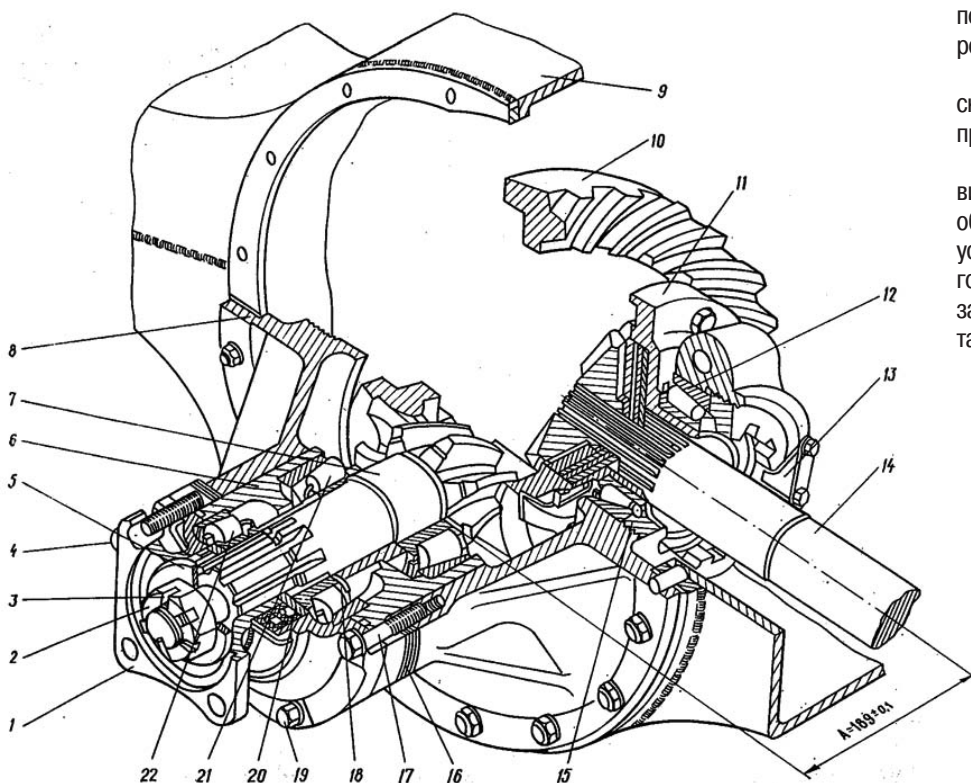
Регулировка главной передачи: 1 — фланец; 2 — гайка; 3 — шплинт; 4, 17, 19 — болт; 5 — шайба; 6 — стакан; 7 — шестерня ведущая; 8 — корпус главной передачи; 9 — корпус моста; 10 — шестерня ведомая; 11 — дифференциал; 12, 21, 22 — подшипник; 13 — крышка подшипника; 14 — полуось; 15 — гайка регулировочная; 16, 18 — прокладка регулировочная; 20 — крышка
